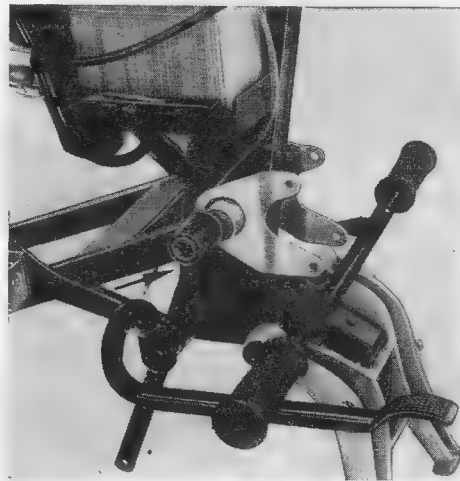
Hinterradschwinge in Pfeilrichtung aufschieben, Druckringe bereits entfernt
